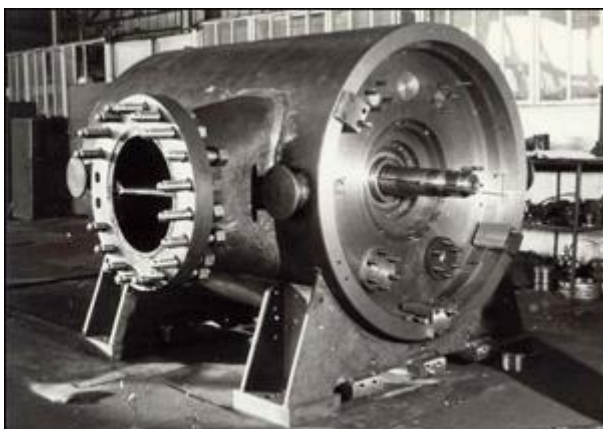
а. Корпус нагнетателя газоперекачивающего агрегата в процессе сборки
